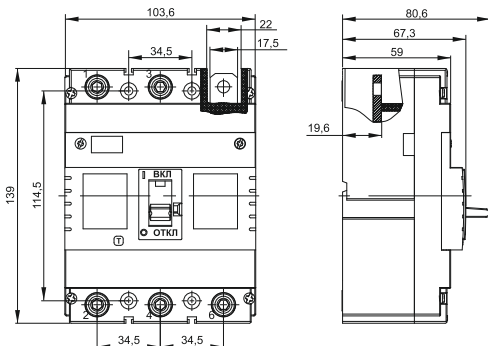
Габаритные и установочные размеры выключателя VA44-35 / Figure 7 — Overall and installation dimensions of the switch VA44-35 / 7-сурет — BA44-35 ажыратқышының габариттік және орнатқыш өлшемдері / Figura 7 — Dimensiunile generale și de montare ale întreruptorului VA44-35
